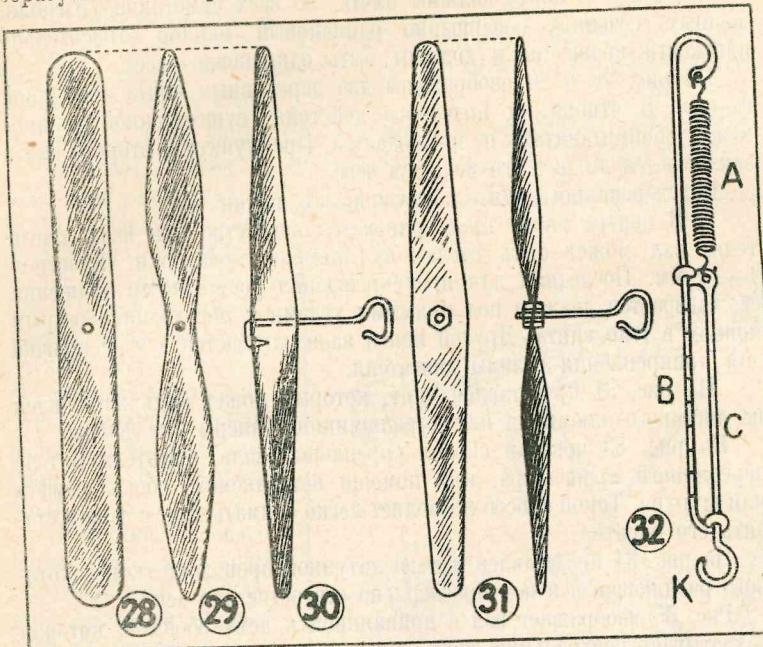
и 29. Деревянные воздушные винты с лопастями различной формы (вид спереди). Рис. 30. Вид сбоку деревянного воздушного винта. Рис. 31. Металлический воздушный винт. Рис. 32. Динамометр.
